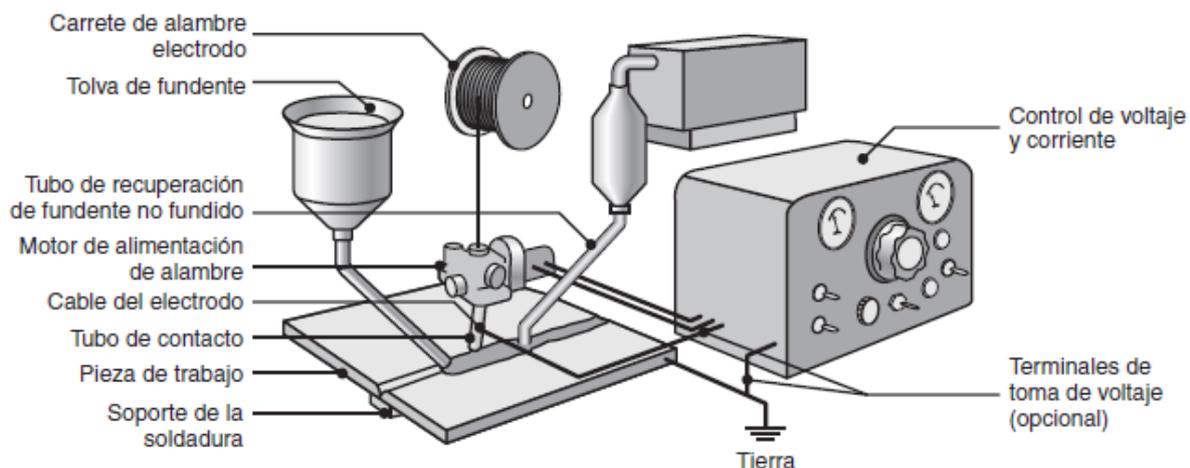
Soldadura por arco sumergido (Fuente: Manufactura, Ingeniería y Tecnología)
